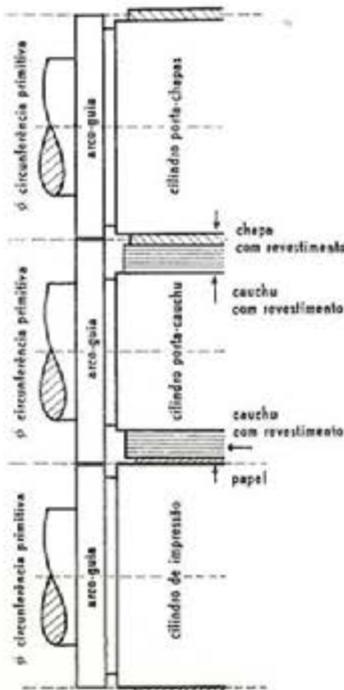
Esquema dos cilindros de uma máquina offset, de rotação, com os aros de guia em contacto.
